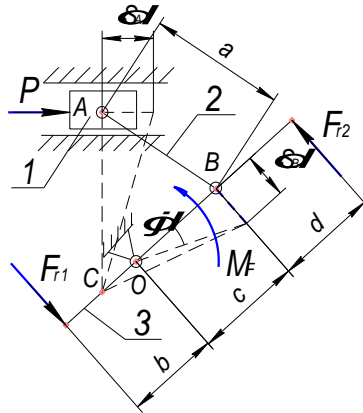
Розрахункова схема натяжного механізму: 1 – повзун; 2 – сполучна ланка; 3 – коромисло
